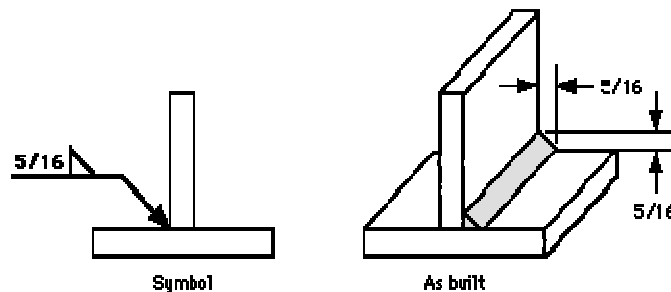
Aplicación de símbolos de soldadura de filete
